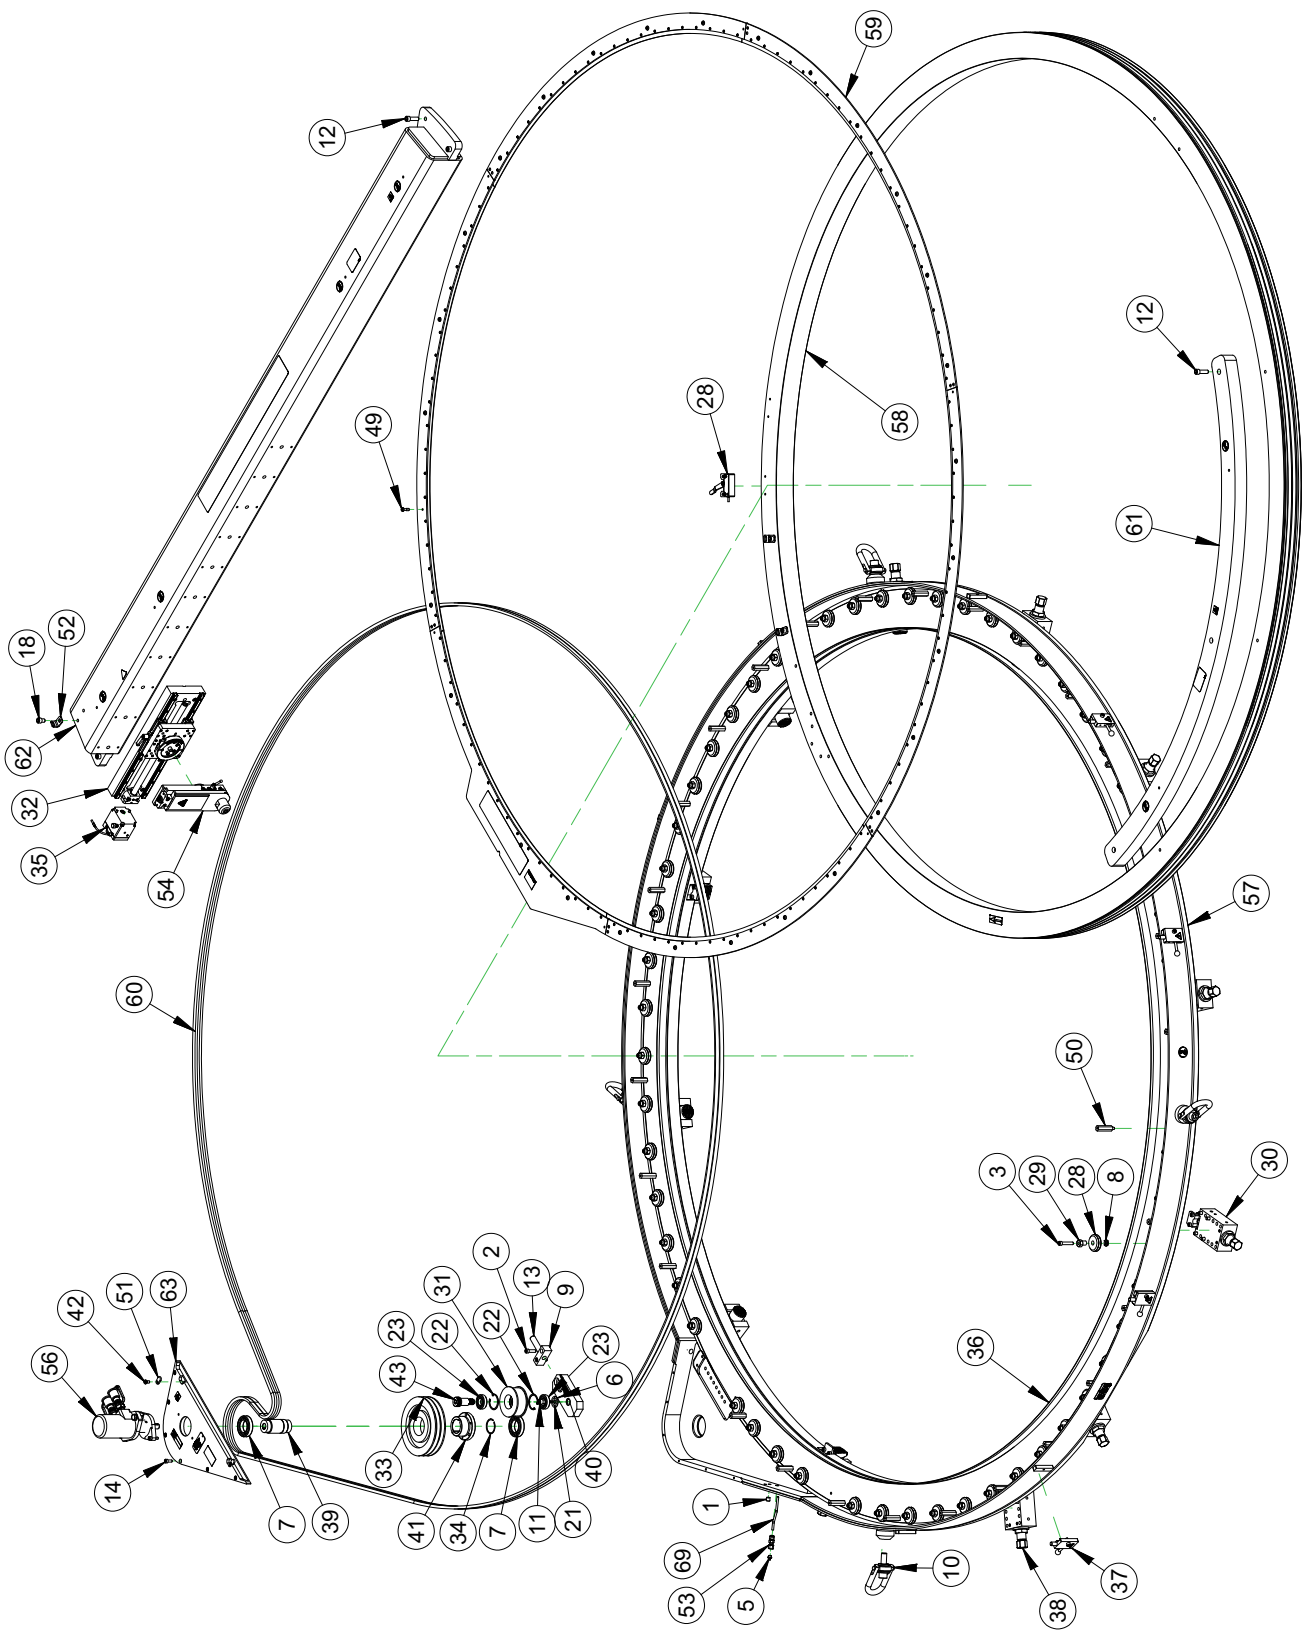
CONJUNTO ODF120 SPEED FACER (N/P 7639-S1)
